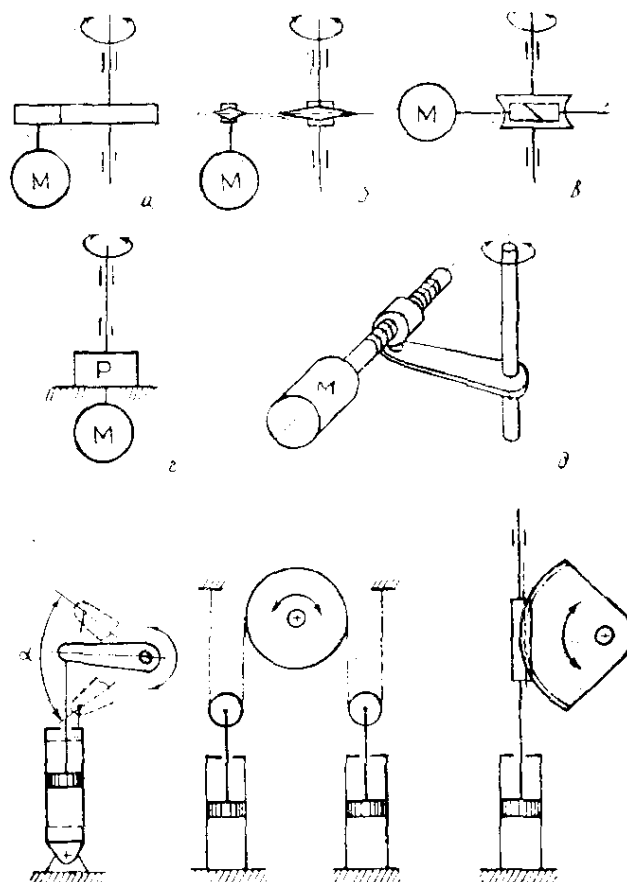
Схеми пристроїв для забезпечення обертального руху ланок маніпулятора
